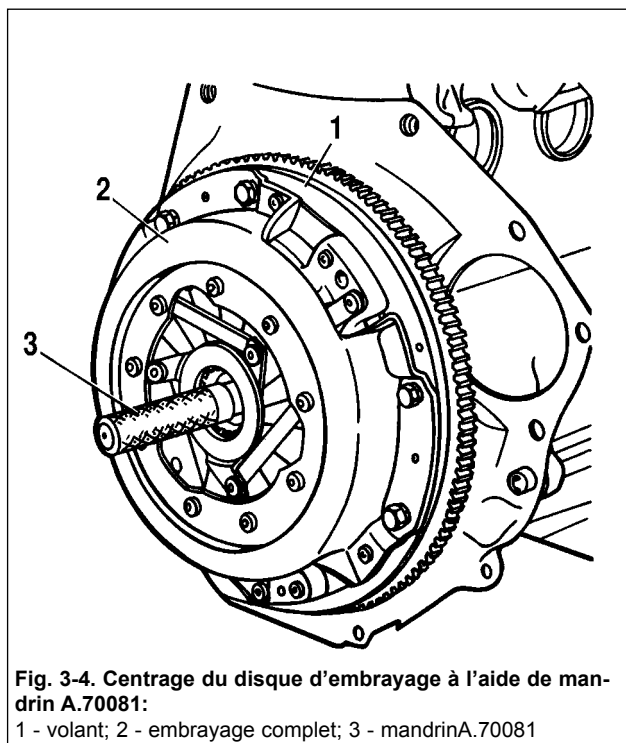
Centrage du disque d'embrayage à l'aide de mandrin A.70081:
